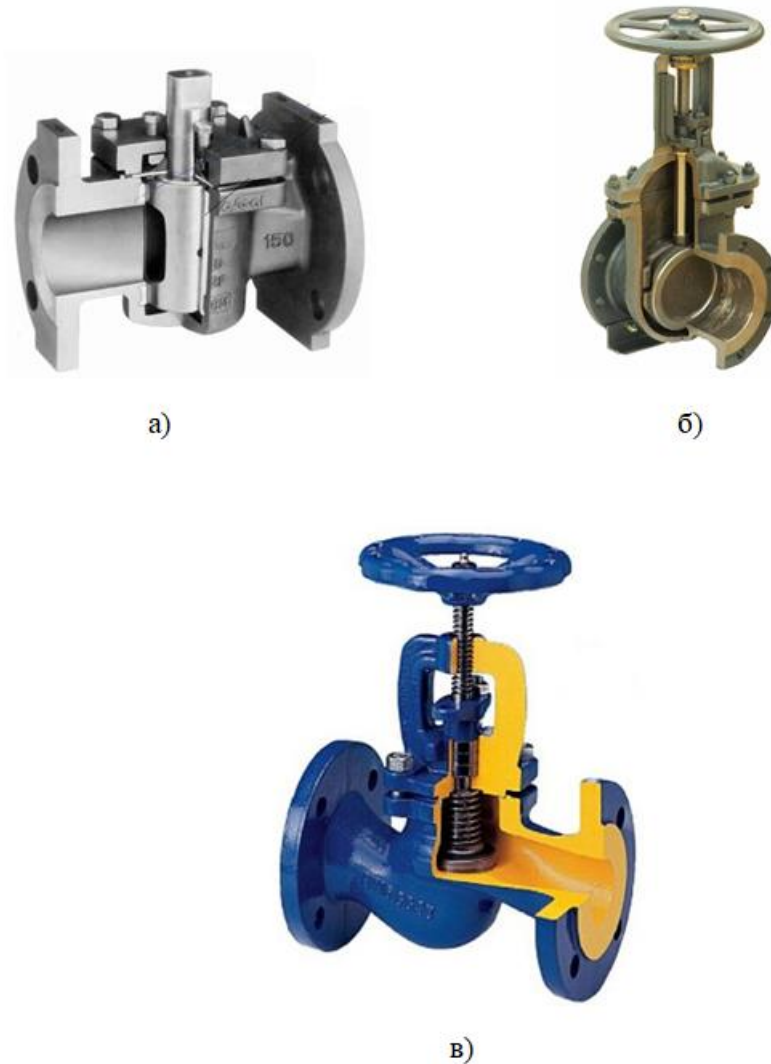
Запірна арматура: а – кран; б – засувка; в – вентиль
